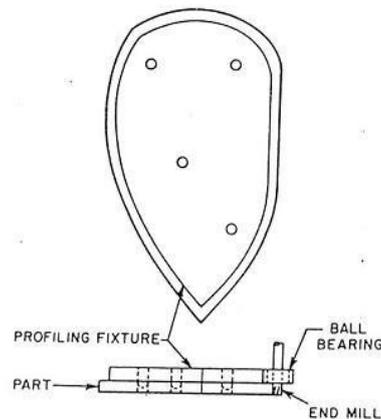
Komponen mesin dengan menggunakan *Fixture
